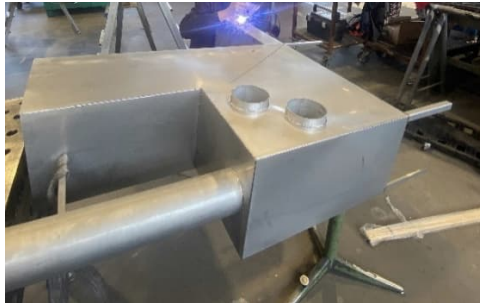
Anschweißen Befestigungswinkel um den Ofen vollständig im Wasser schweben zu lassen, so dass die bestmögliche Wärmeabstrahlung erreicht werden kann
